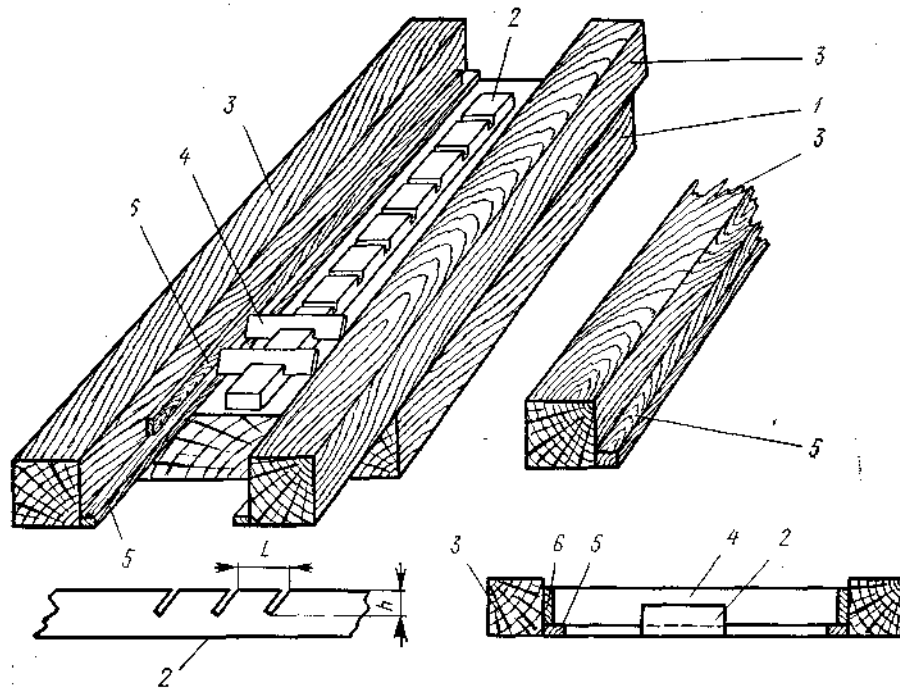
Шаблон-кондуктор для сборки внутренних трапов:
